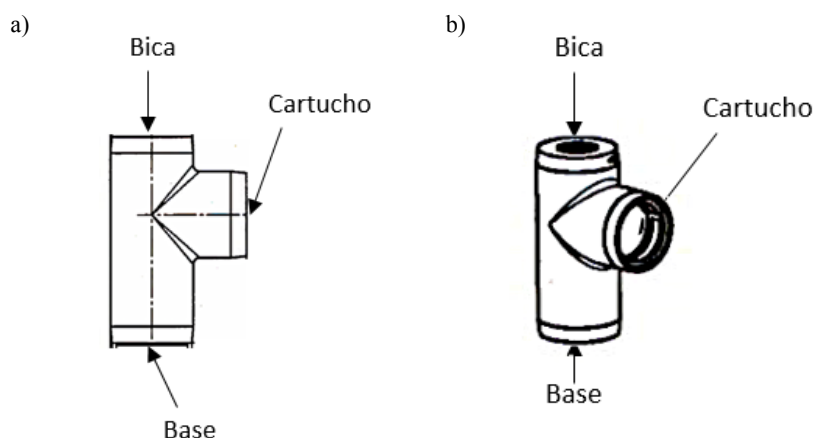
Desenho da peça a maquinar: a)2D; b) 3D.
